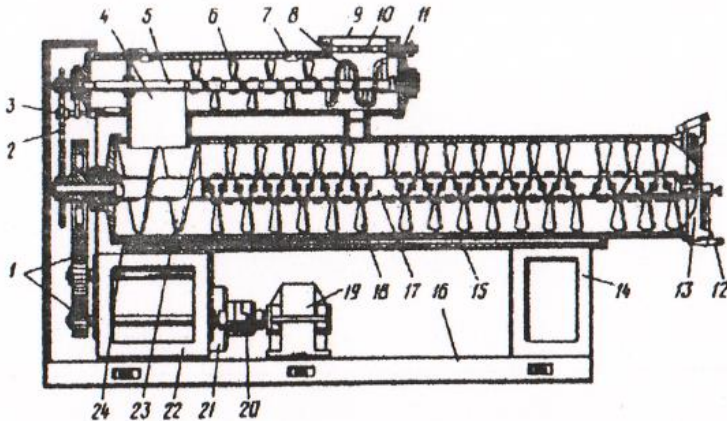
Тістомісильна машина ШТ-1М: 1 – зубчаста передача; 2 – ланцюгова передача; 3 – натискна зірочка; 4 – патрубок; 5 – вал; 6 – лопаті; 7 – камера попереднього змішування; 8 – стрічковий шнек; 9 – завантажувальний патрубок; 10 – перфорована труба; 11 – штуцер; 12 – важіль; 13 – кришка; 14, 22 – стійки; 15 – водяна сорочка; 16 – фундаментна плита; 17 – місильний вал; 18 – лопаті; 19 – редуктор; 20 – муфта; 21 – електродвигун; 23 – шнек; 24 – місильна камера
